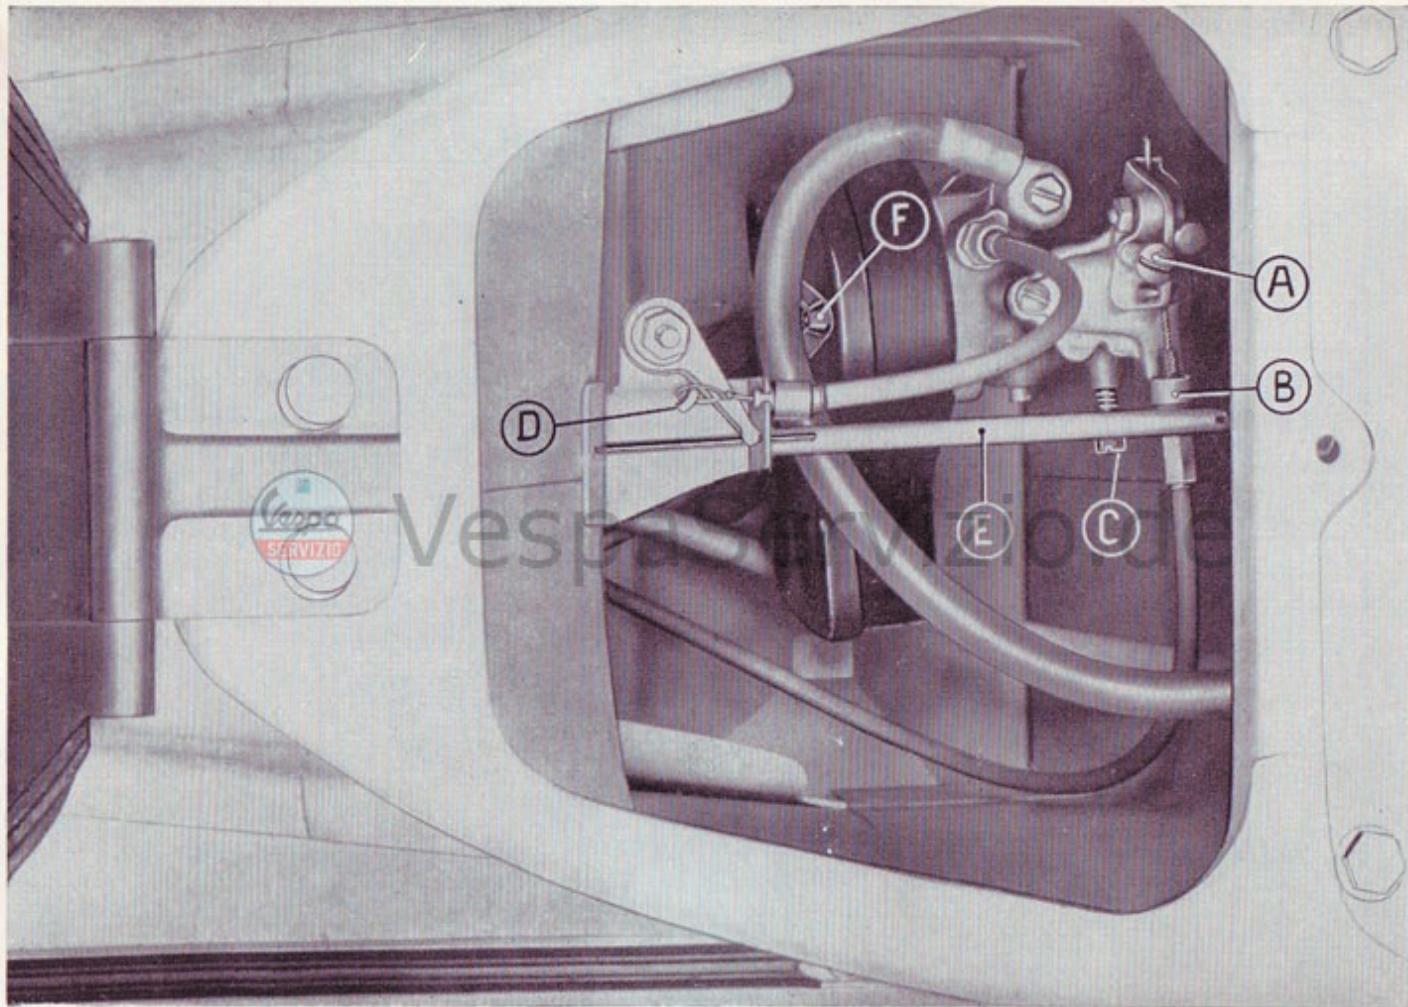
Comment accéder à l'ensemble carburateur - filtre à air (voir normes à page 24 et 32).
